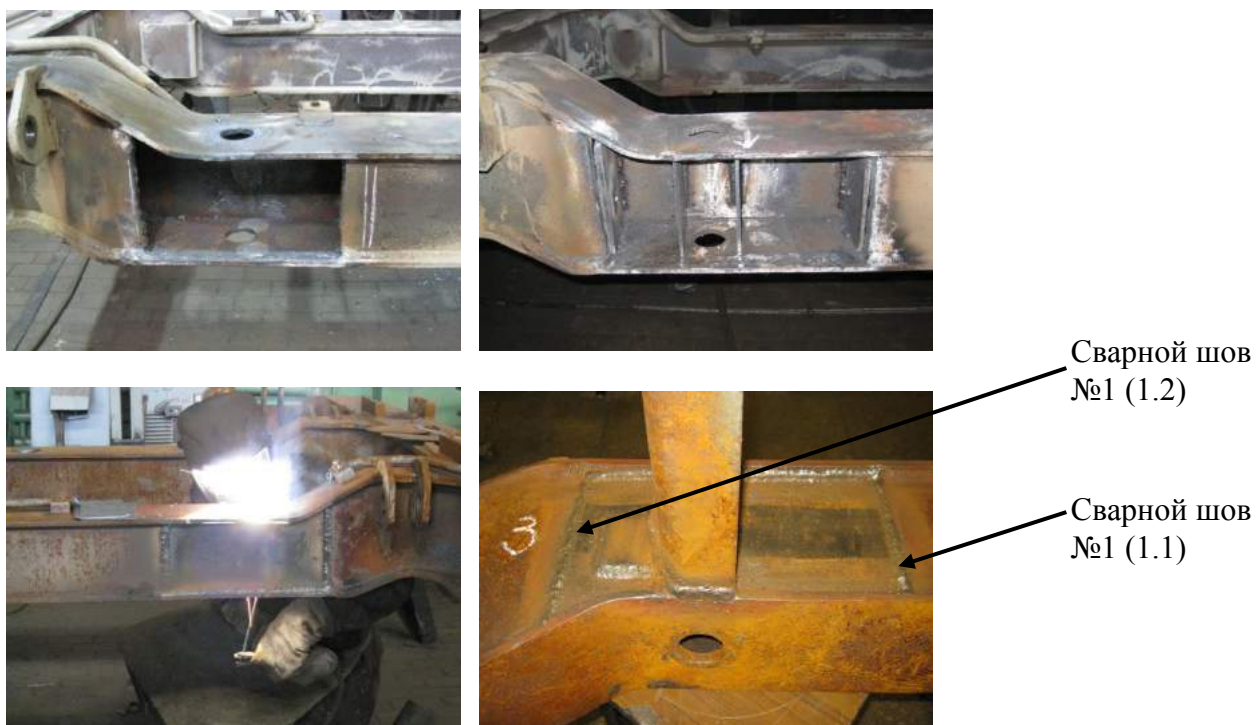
Технология ремонта на вертикальной стенке поперечной балки и сварные соединения ремонтной вставки с остающейся подкладкой (сварной шов №1)
